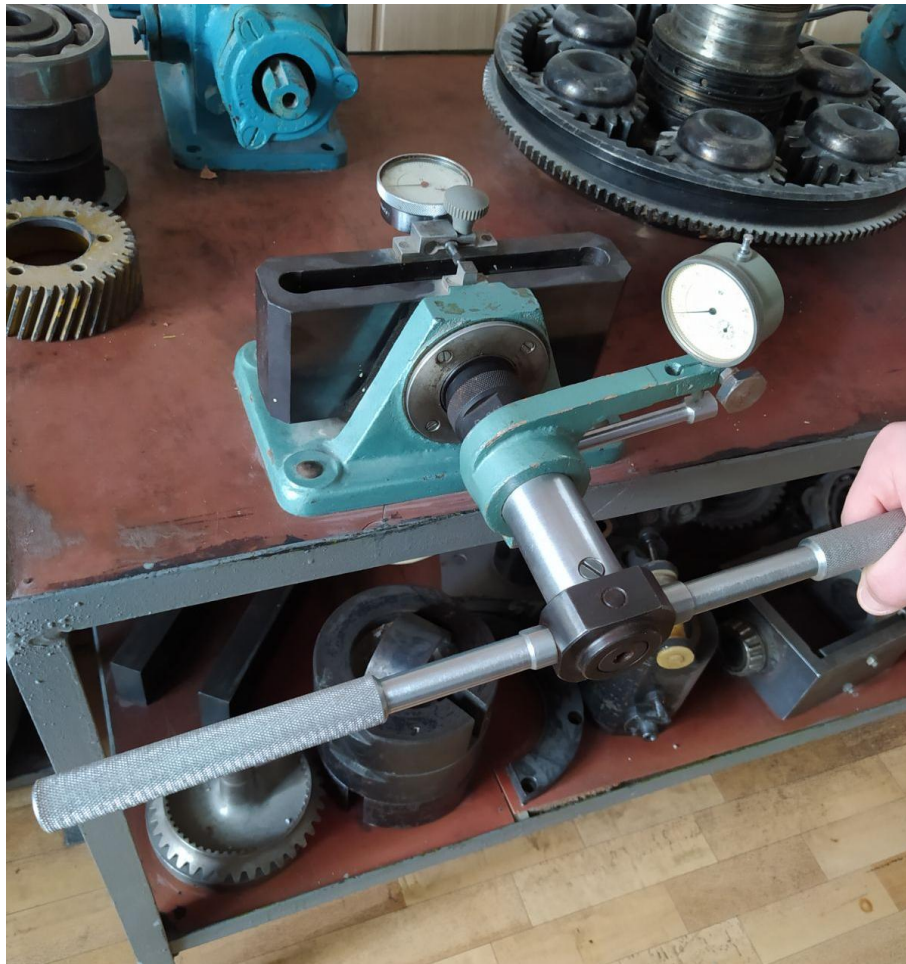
Установка ДМ 27 підготовлена до роботи
